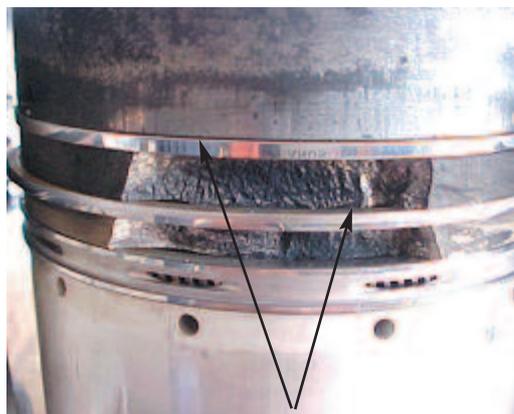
Paredes entre ranuras fracturadas en pistón aplicado en motores Diesel
